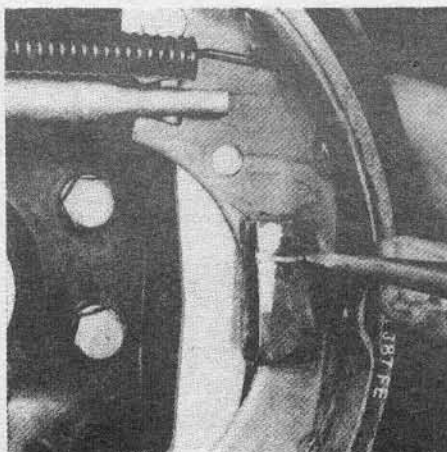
б Оттяните держатель пружины отверткой, затем поверните палец натяжителя до совпадения его головки с прорезью в держателе - пружина должна издать характерный звук при сжатии натяжителя (повторите с другой пружины).
